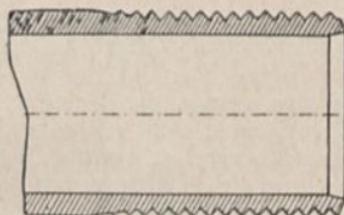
Konisch auslaufendes, zylindrisches Gewinde auf stumpf geschweißtem Rohr.
